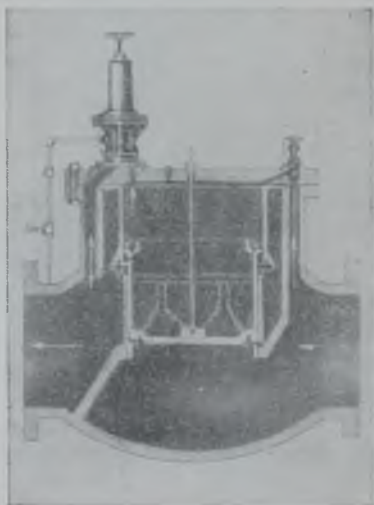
Редукционный клапан для понижения давления (по материалам Golden-Anderson Valve Specialty Co.)
